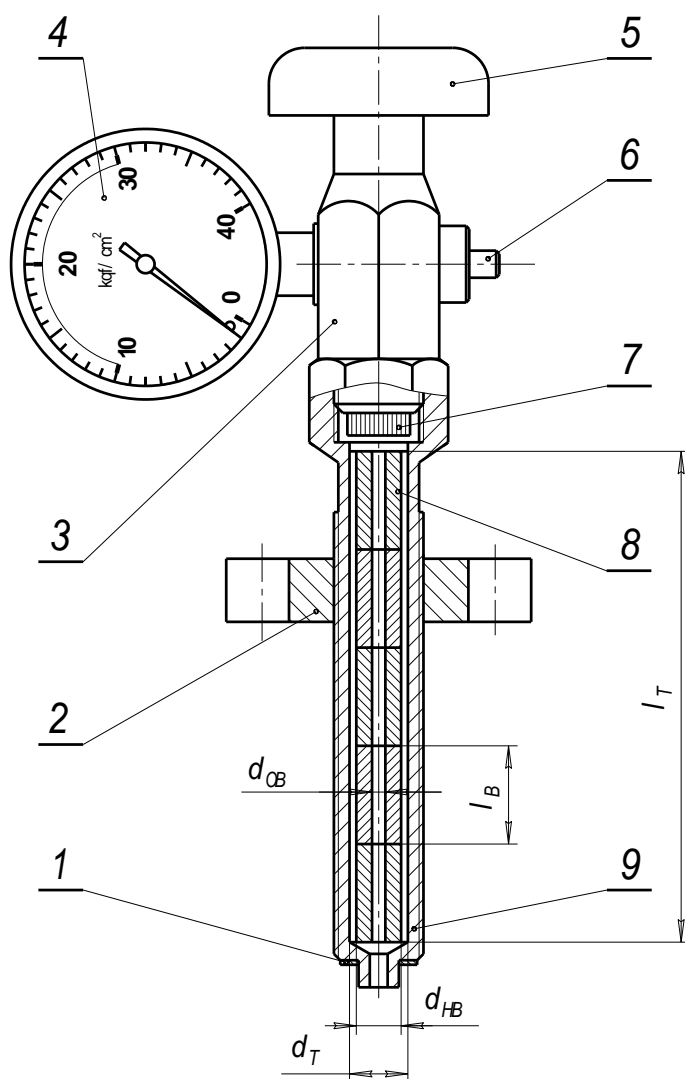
Компрессометр КИ-28125, подготовленный к испытаниям:
